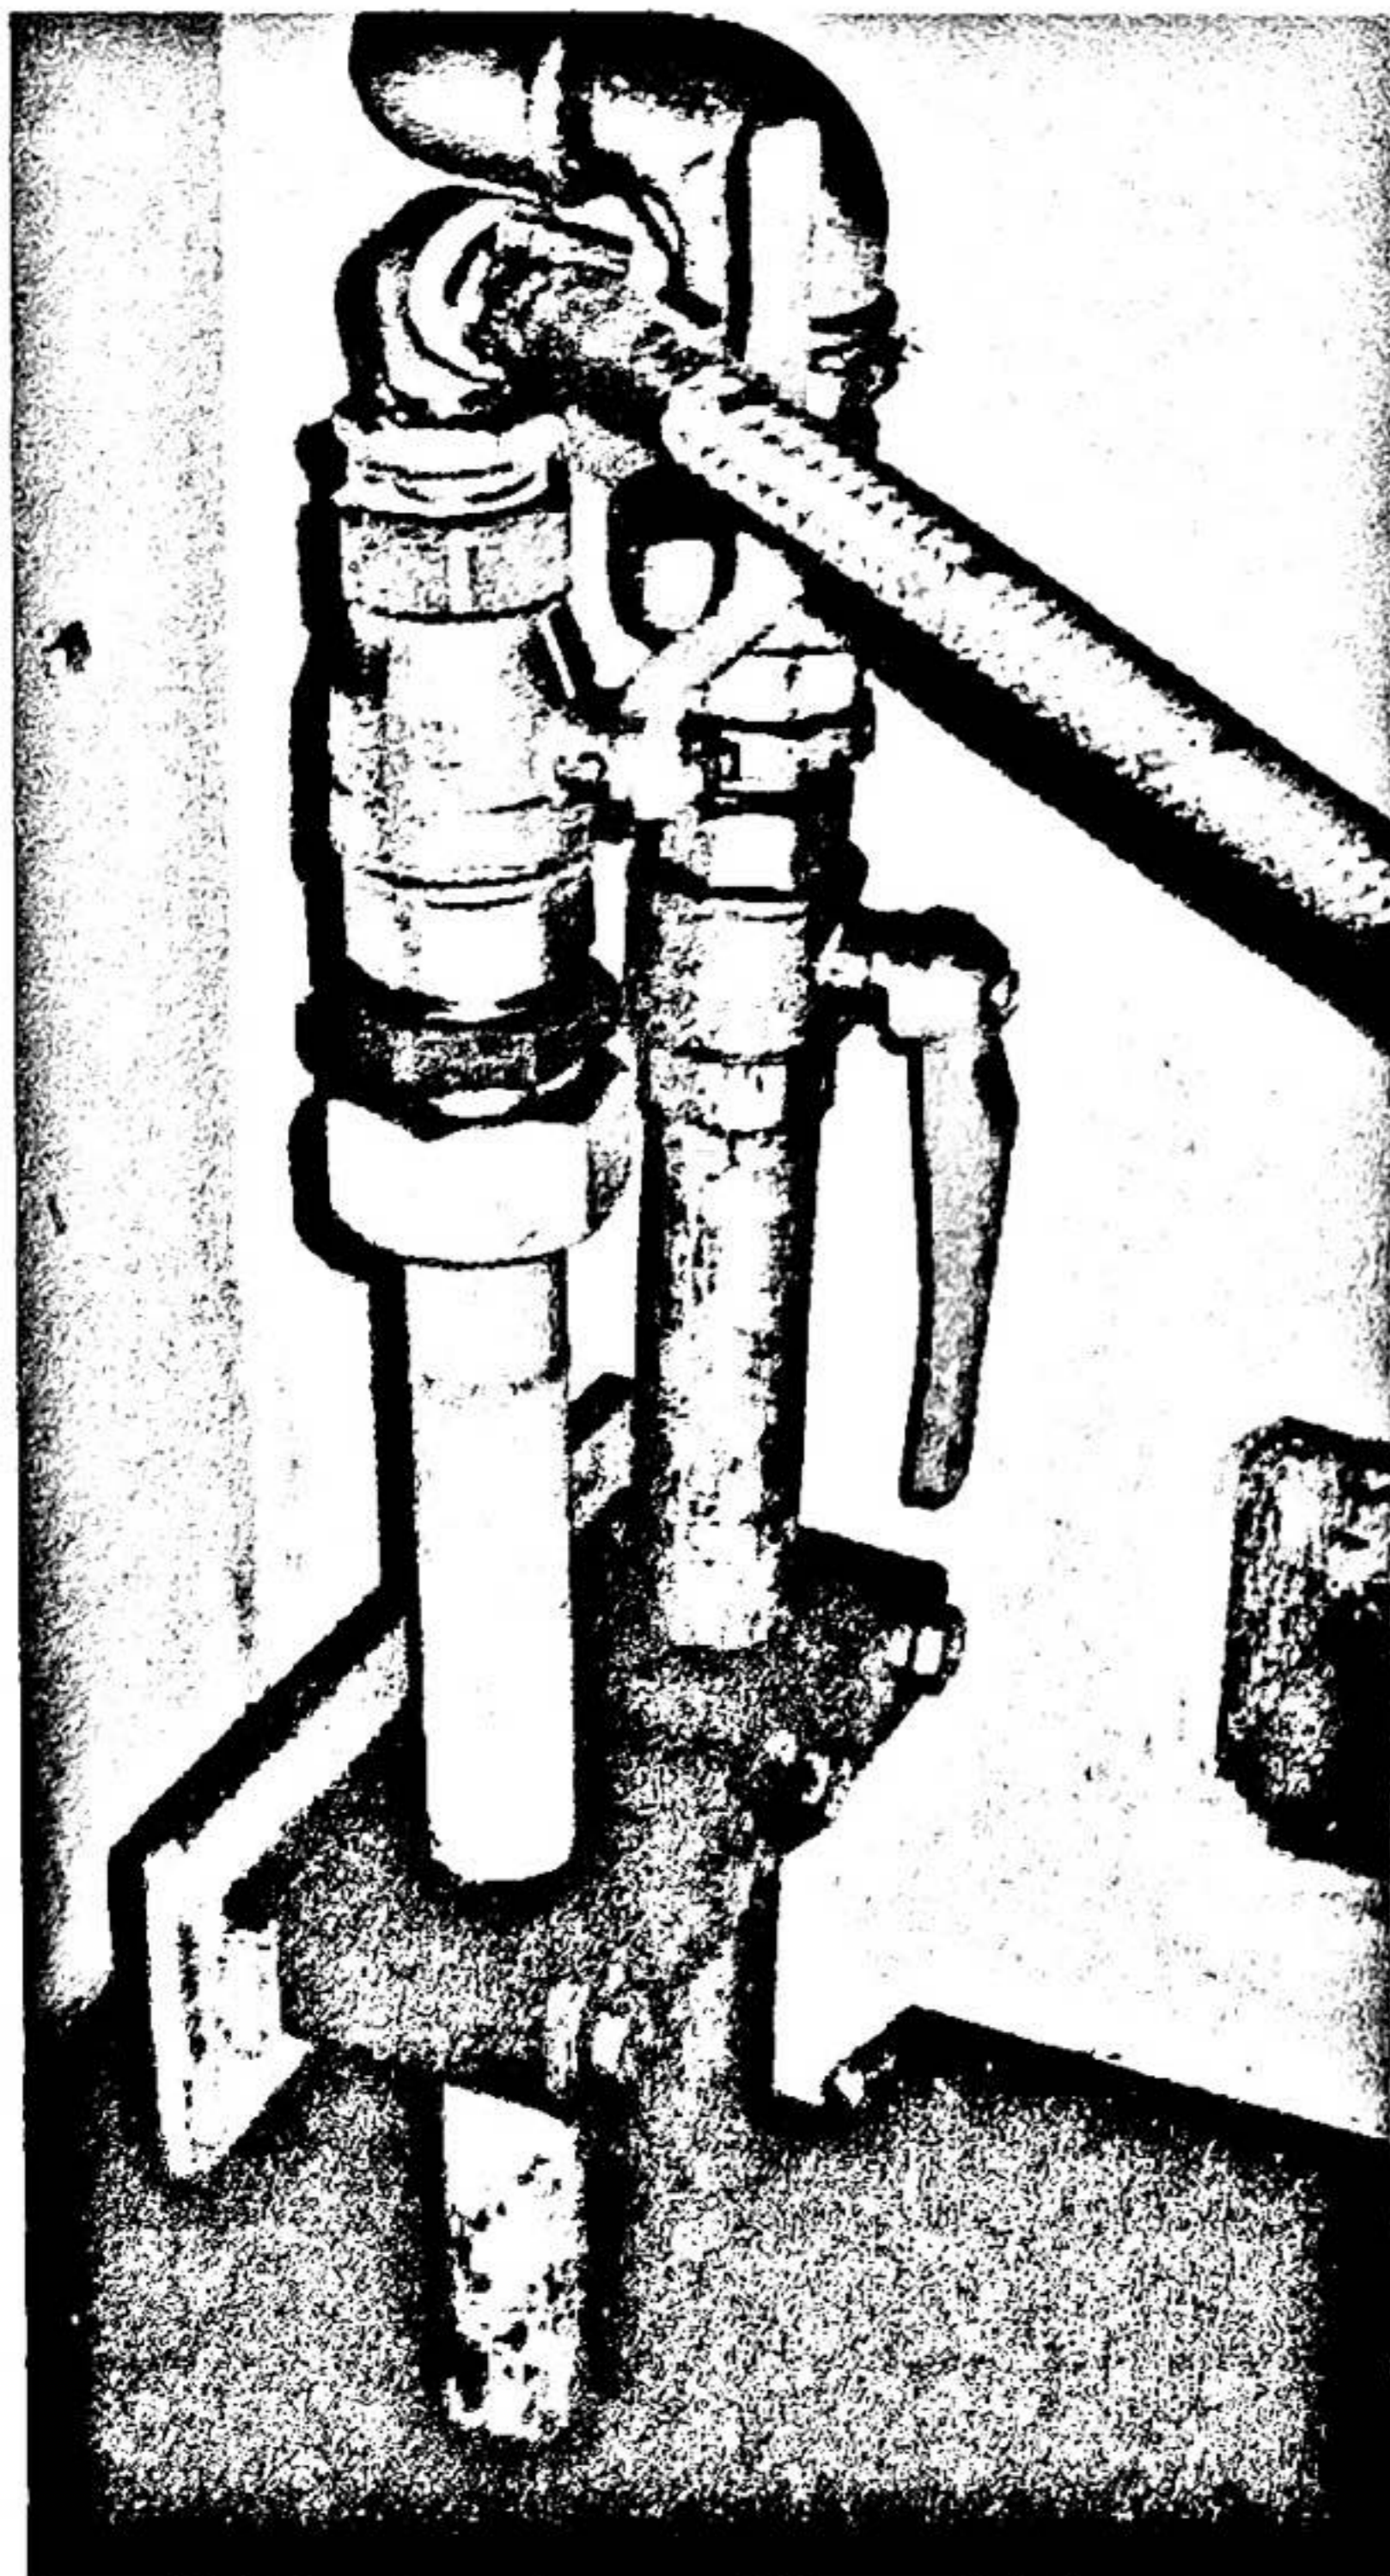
/14: Anschlüsse für die Bohremulsion zur Spänespülung (rechts), für Druckluft (links mit Schlauch) (neben dem Spindelkasten)
